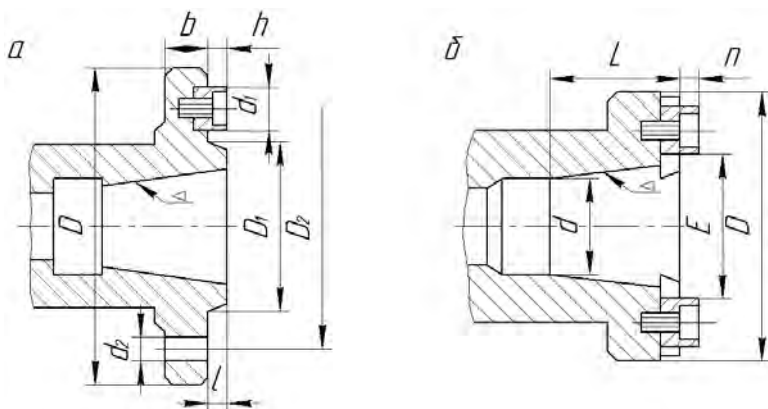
Форма передних концов шпинделей под поворотную шайбу с цилиндрической шпонкой для токарных (а) и с двумя призматическими шпонками для фрезерных и многооперационных сверльно-фрезерно-расточных станков (б)
